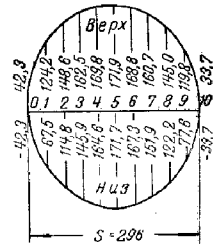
Развертка отверстия в стволе сварного тройника.
